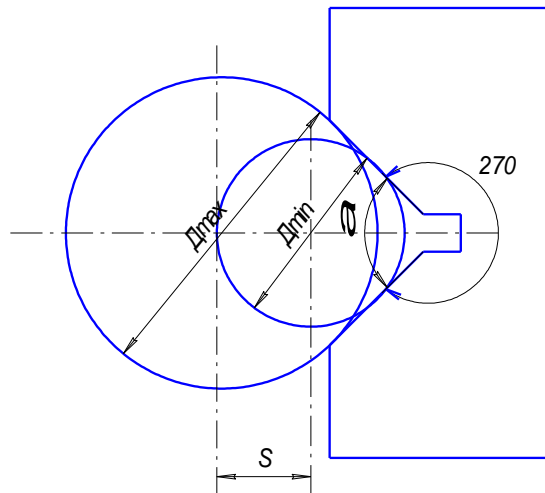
Схема установки контрольованої деталі в призмі
